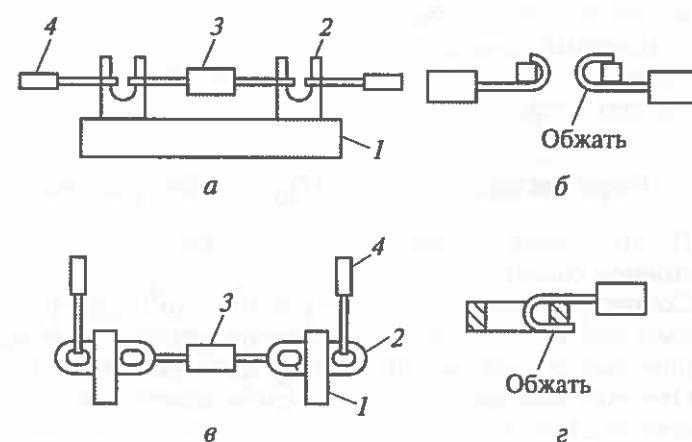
Варианты механического крепления выводов элементов и монтажных проводов на монтажной плате с опорными элементами:
